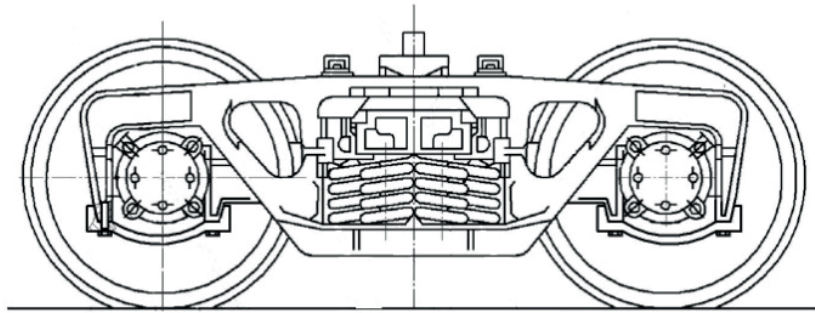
Схема візка типу 18-100 з буксовою стрункою
